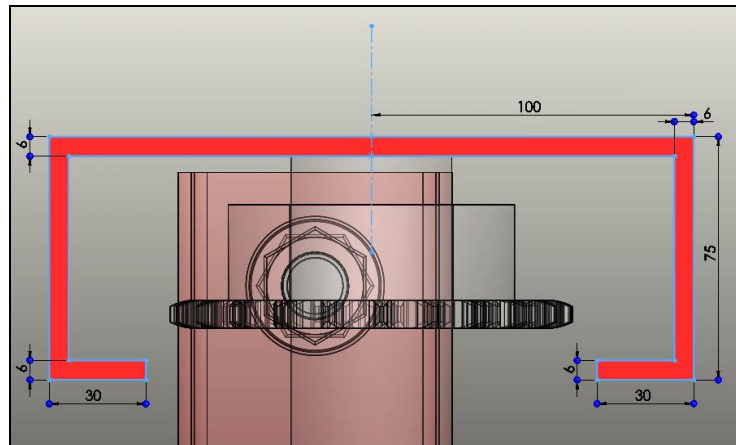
VISTA DE SECCIÓN DE LA VIGA SELECCIONADA
